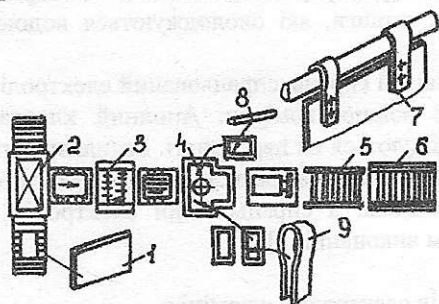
Схема лінії для складання катодів: 1-основа; 2-установка для видачі основ; 3-зигочна машина; 4-складально-клепальний автомат; 5-транспортер завіски; 6-стелаж-накопичувач; 7-складений катод; 8-штанга; 9-вушко
